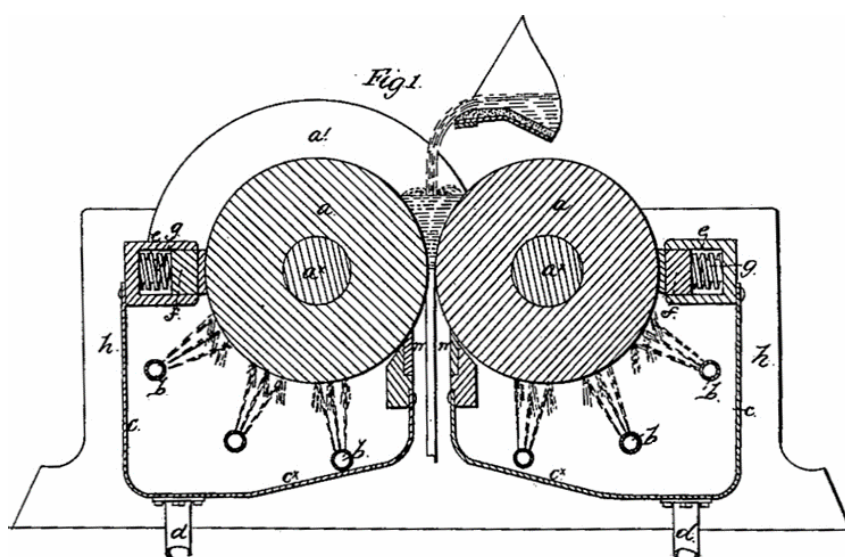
Первый эскиз машины валковой разливки-прокатки (1865 г.):
